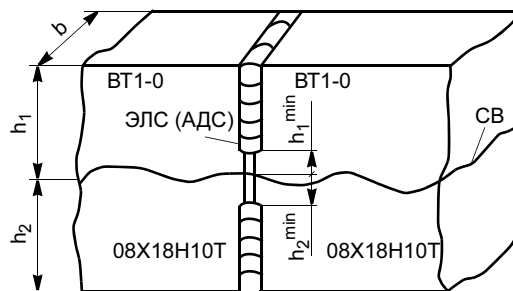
Схема стыкового соединения биметаллических титаностальных полос, выполненного электронно-лучевой или аргонодуговой сваркой
